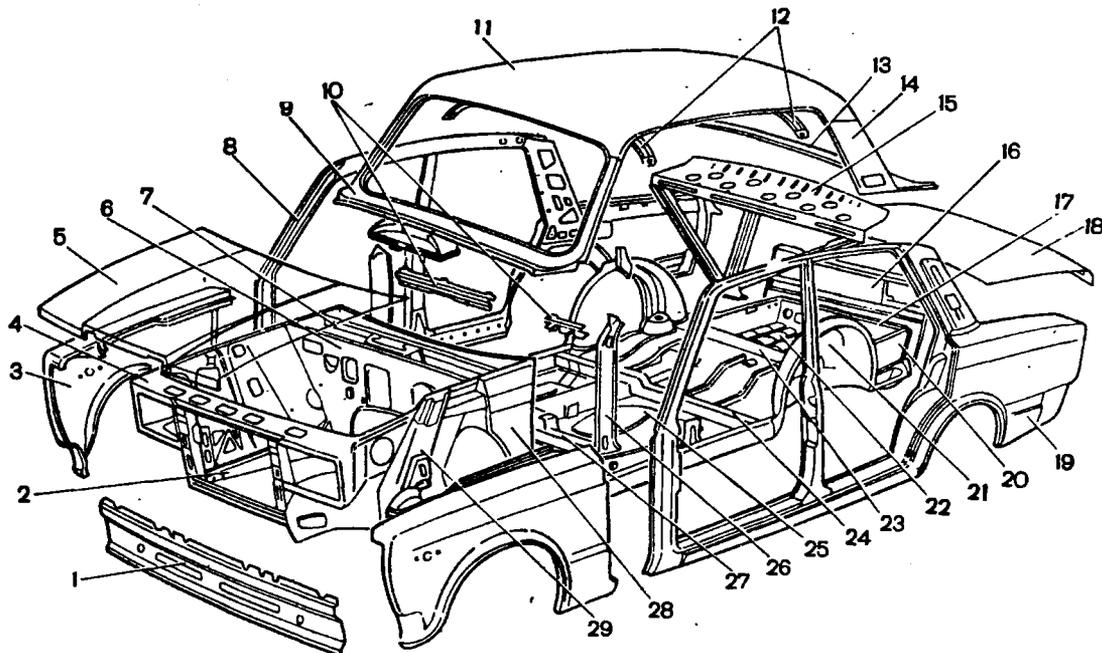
Детали каркаса кузова: 1 - панель облицовки передка; 2 - передний лонжерон; 3 - переднее крыло; 4 - верхняя поперечина передка; 5 - капот; 6 - щиток передка в сборе; 7 - коробка воздухопритока; 8 - боковина кузова; 9 - рамка ветрового окна; 10 - поперечина панели приборов; 11 - панель крыши; 12 - усилители крыши; 13 - рамка заднего окна; 14 - боковая панель крыши; 15 - полка задка с раскосами; 16 - панель задка; 17 - нижняя поперечина задка; 18 - крышка багажника; 19 - заднее крыло с боковиной; 20 - лонжерон заднего пола; 21 - арка заднего колеса; 22 - пол багажника; 23 - поперечина над задним мостом; 24 - поперечина под задним сиденьем; 25 - панель пола; 26 - накладка передней стойки; 27 - поперечина под передним сиденьем; 28 - боковая панель передка; 29 - брызговик переднего крыла со стойкой в сборе
